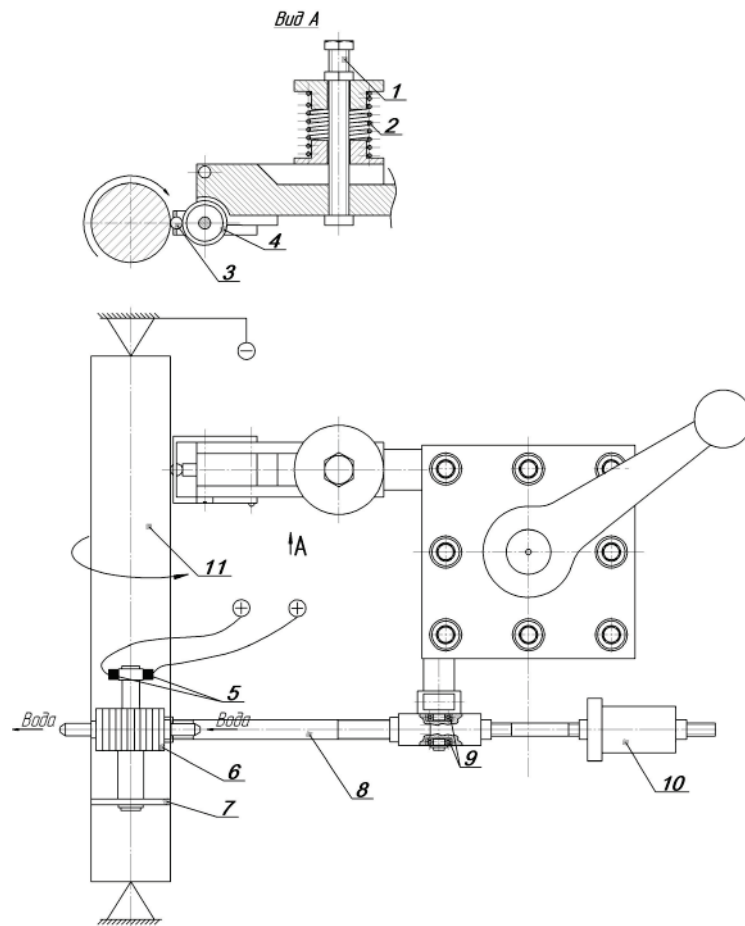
Схема установки для формування комбінованого зносостійкого покриття на валах:
